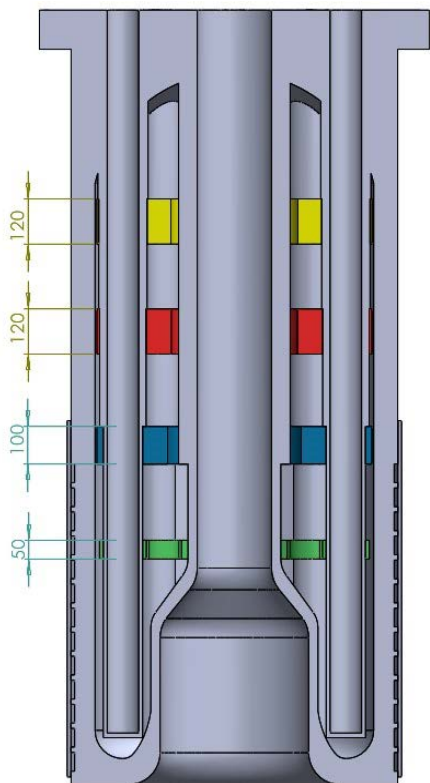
Конструктивная схема оптимизированного корпуса АЗ ВИР-3
